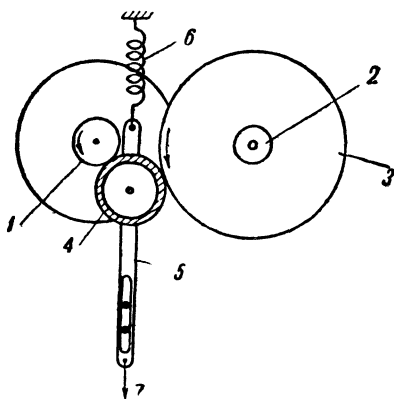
Передача вращения от двигателя к ведущему ролику через паразитный обрезиненный ролик: 1 — ось двигателя; 2 — ведущий ролик; 3 — шкив ведущего ролика (сталь, чугун); 4 — паразитный ролик; 5 — направляющая планка; 6 — удерживающая пружина; 7 — тяга, выключающая и включающая сцепление
